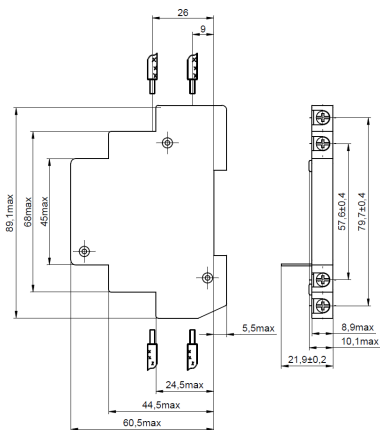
Габаритные, установочные и присоединительные размеры МСК
